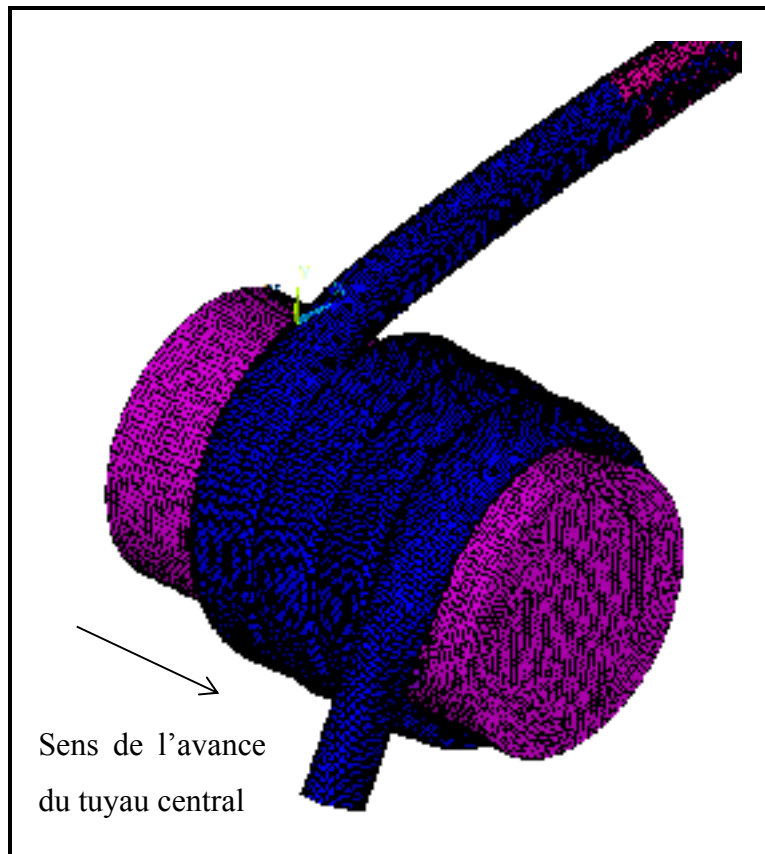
Vue iso d'enroulement hélicoïdal sur 3 tours
